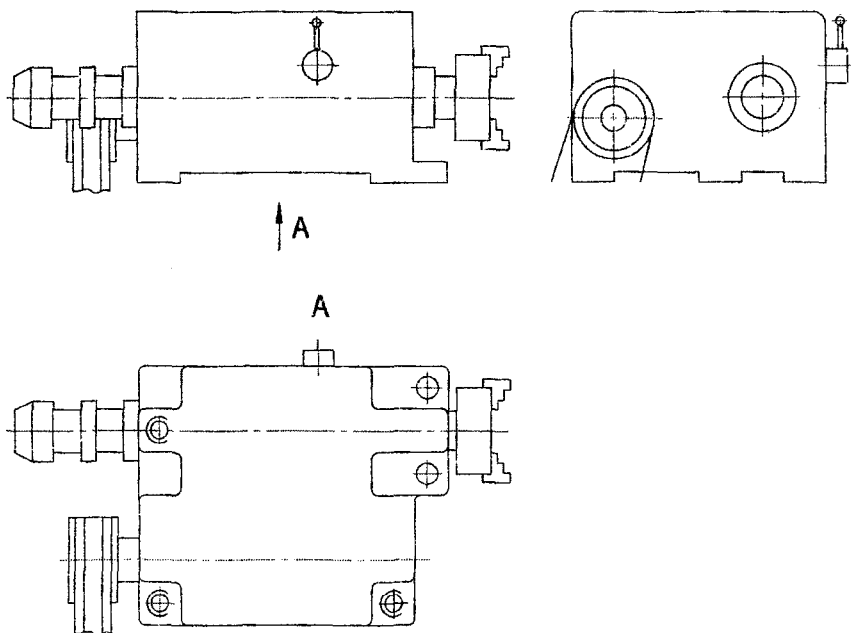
Компоновка шпиндельной бабки токарного станка с ЧПУ
